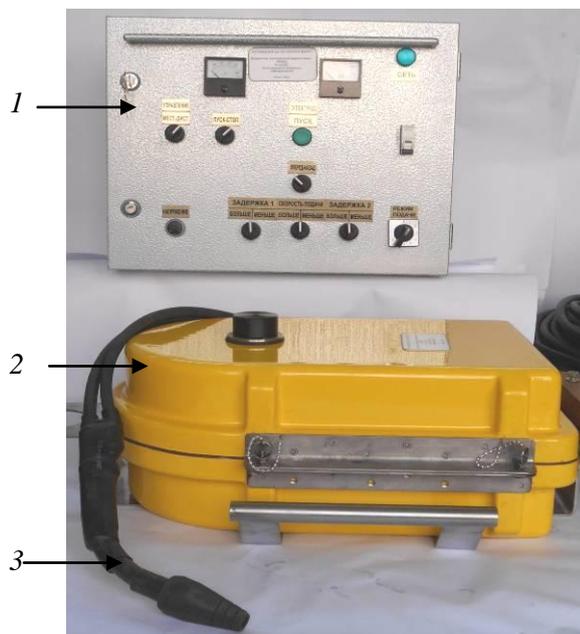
Полуавтомат для подводно сварки и резки: 1 – блок компьютеризованного управления и регулирования; 2 – погружной блок; 3 – специализированный шланговый держатель
